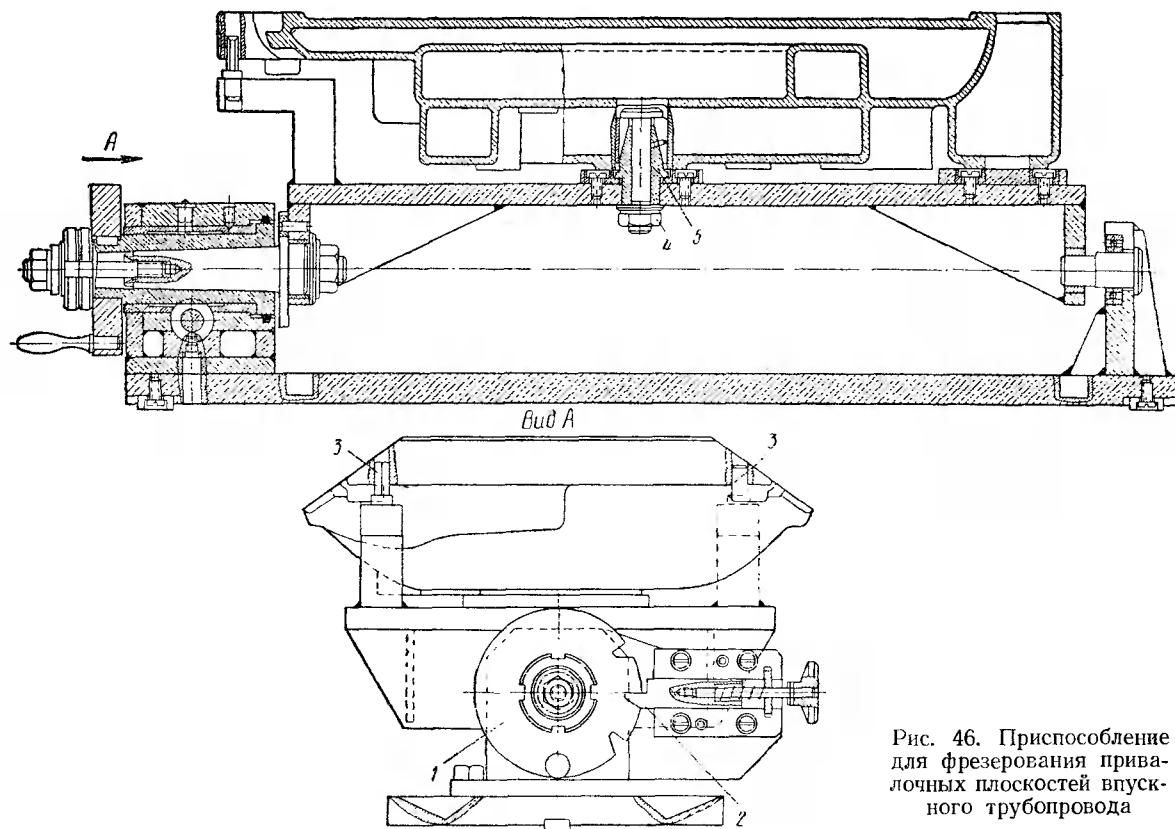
Приспособление для фрезерования привалочных плоскостей впускного трубопровода
